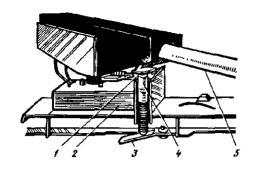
Механизм микролифта: 1 — втулка; 2 — корпус подшилника; 3 — пружина; 4 — шлок; 5 — звукосниматель
